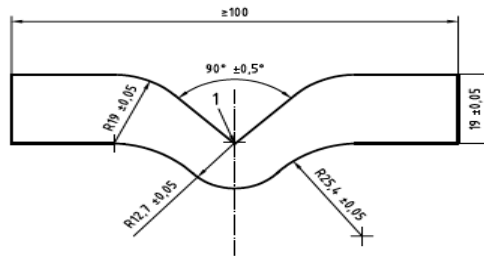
Forma y dimensiones de la probeta del ensayo de rasgado.
